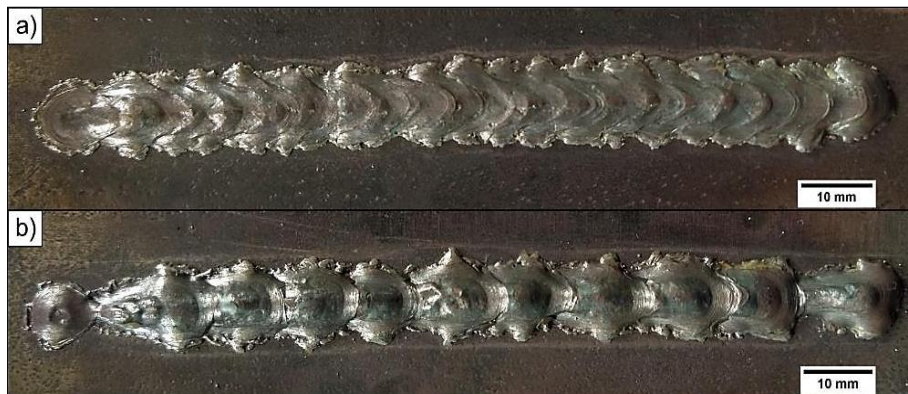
Cordões de solda: a) Avanço 6 e reversão 3; b) avanço 8 e reversão 4
